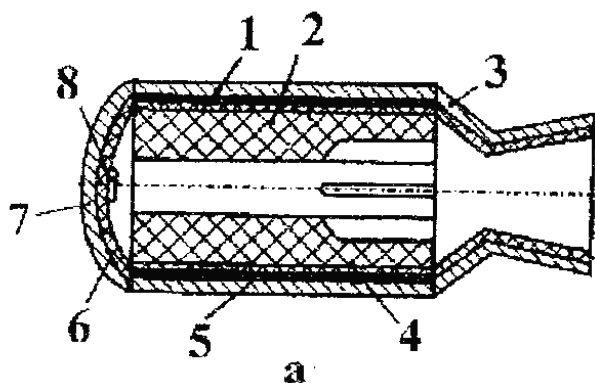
а. Схема заряда, скрепленного с корпусом ракетного двигателя [63]:
